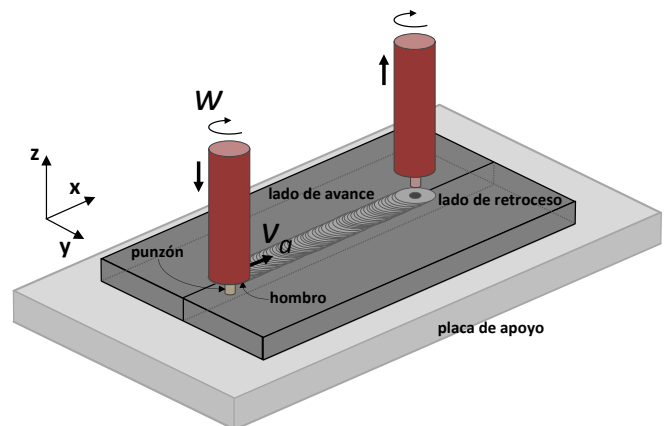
Esquema del proceso de FSW mostrando la disposición de la herramienta al comienzo y al finalizar la soldadura.
